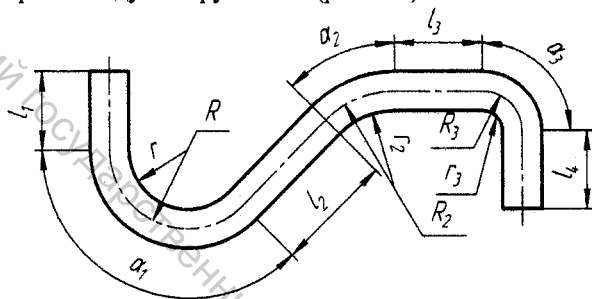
Схема разделения изделия на элементы для определения длины развертки
